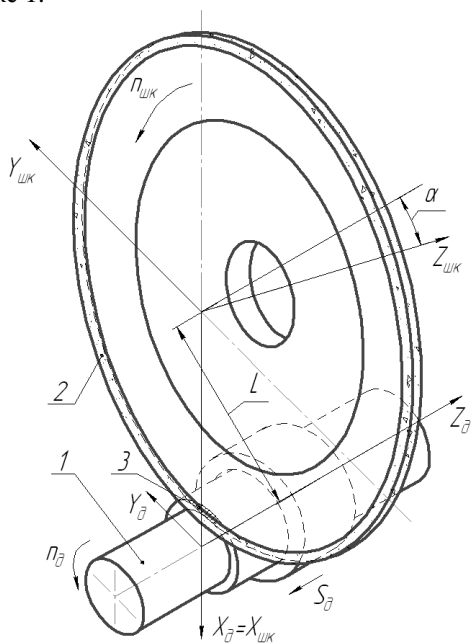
Схема глубинного круглого шлифования ступенчатого валика со скрежывающимися осями инструмента и детали
